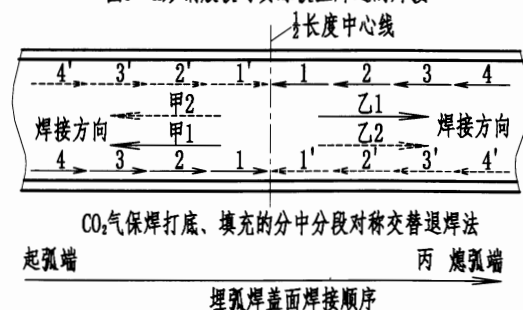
H形钢主焊缝气保焊、埋弧焊具体的焊接顺序
